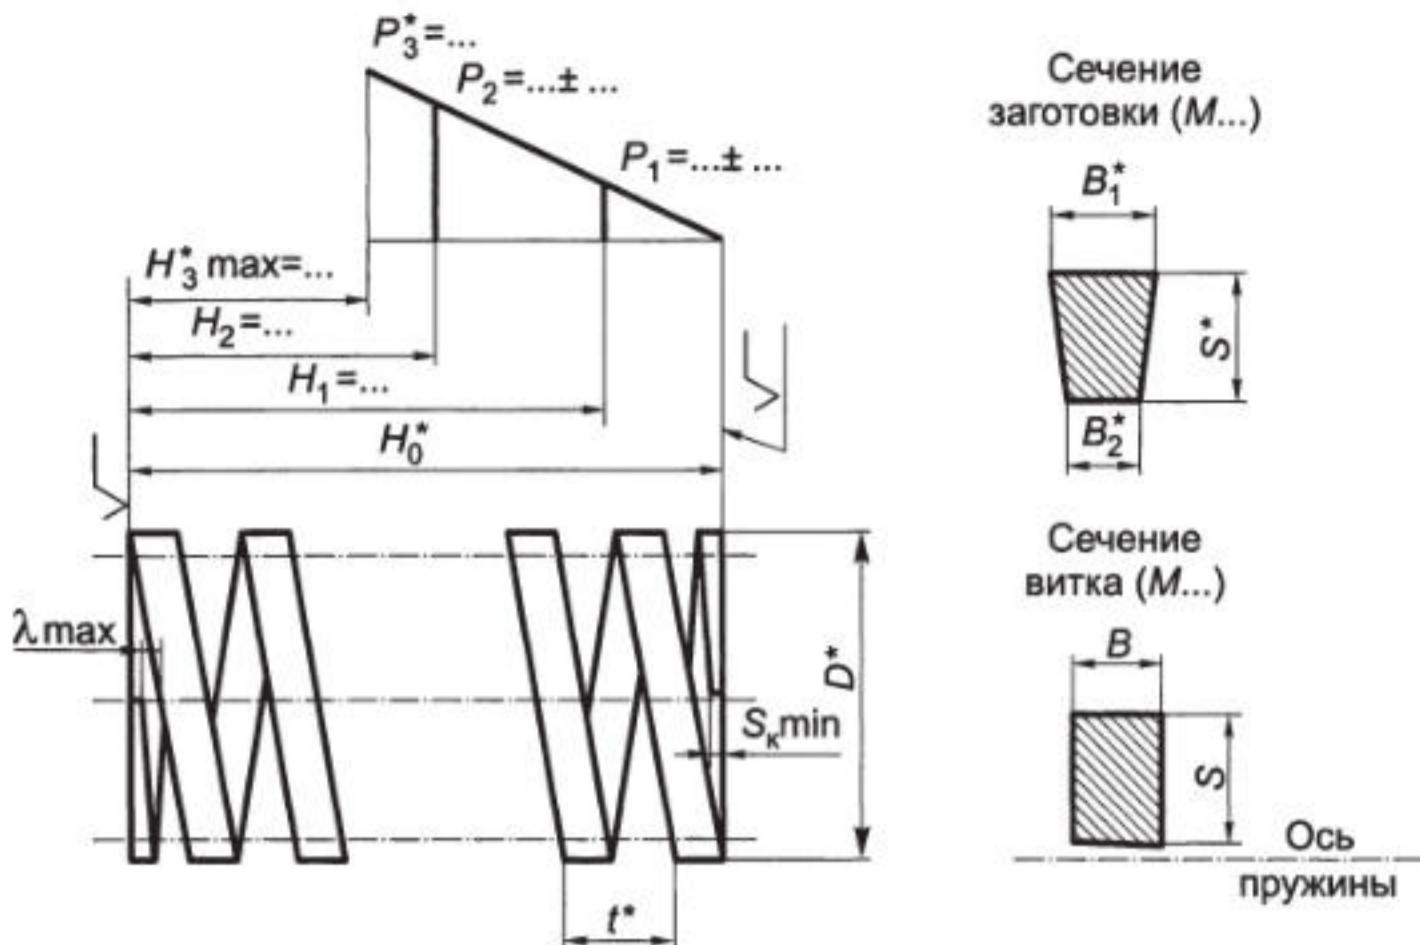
Пружина сжатия с прямоугольным сечением витка с поджатыми на $\frac{3}{4}$ витка концами и шлифованными на $\frac{3}{4}$ окружности опорными поверхностями
